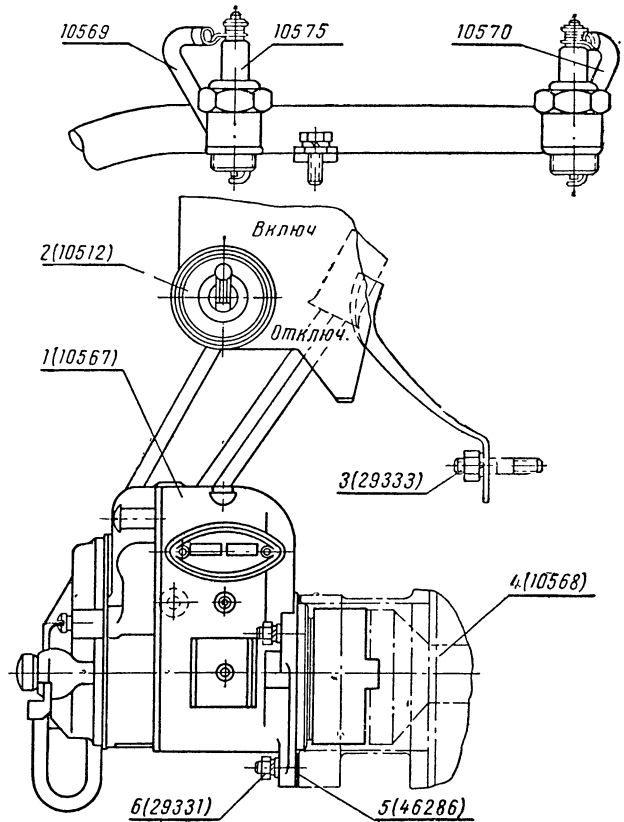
Магнето М-47Б и защитная трубка проводов: 1 — корпус; 2 — замок зажигания; 3 и 6 — шпильки; 4 — валик привода; 5 — прокладка.
